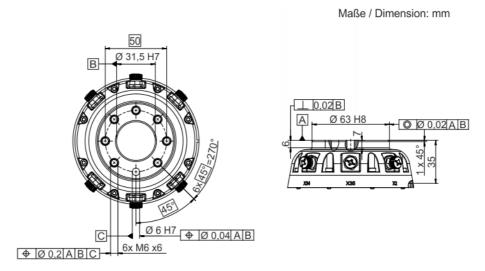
Abmessung, Medien-Flansch elektrisch
